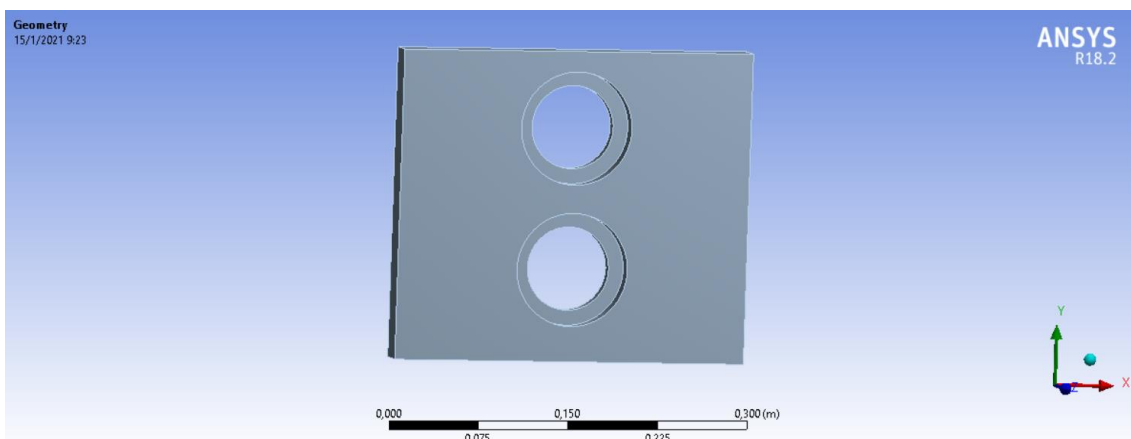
Definición de geometría - bastidor izquierdo de estampado
